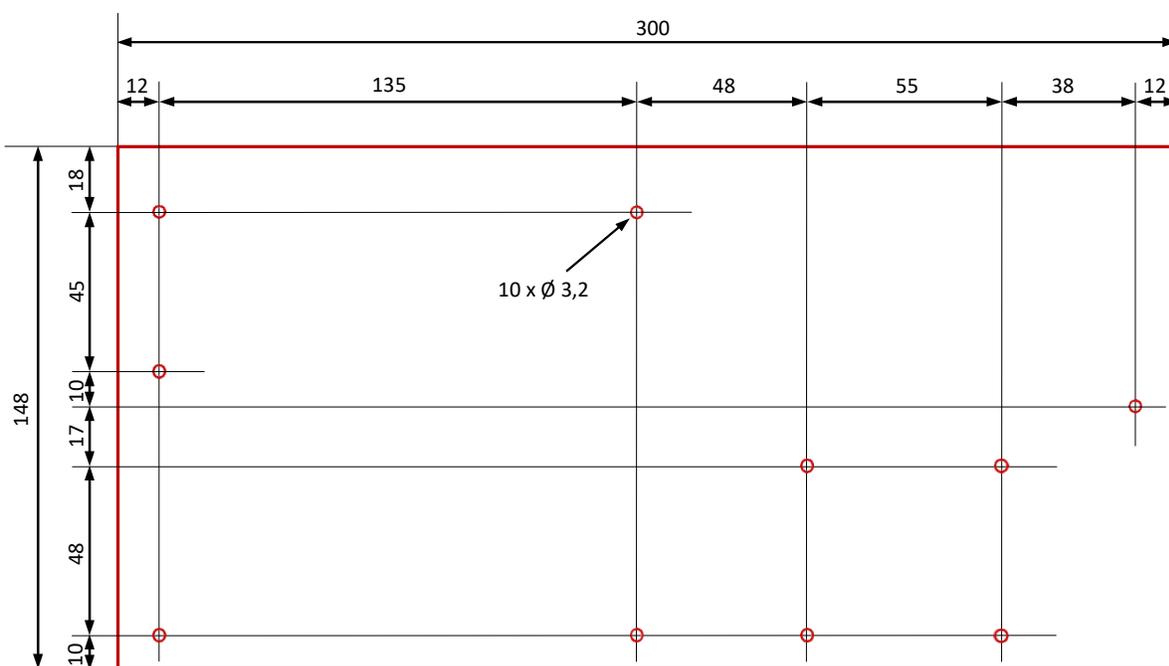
plan de l'usinage de la plaque supportant les deux modules du kit AM8-MKI – Échelle ½
